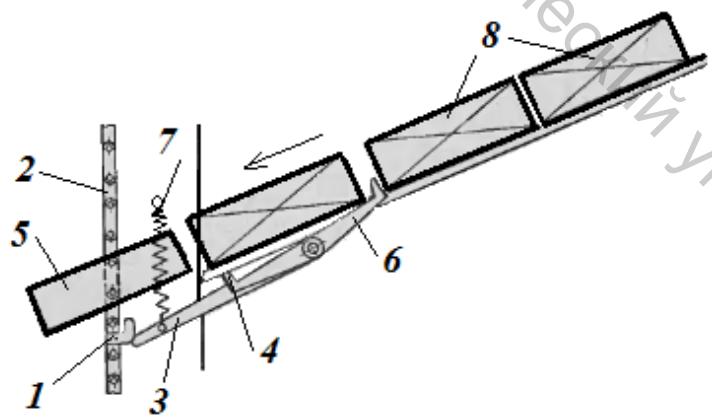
Схема загрузочного устройства элеватора для спуска обуви
